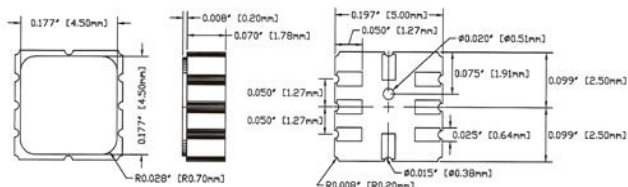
Зовнішній вигляд корпусу акселерометра [27]
